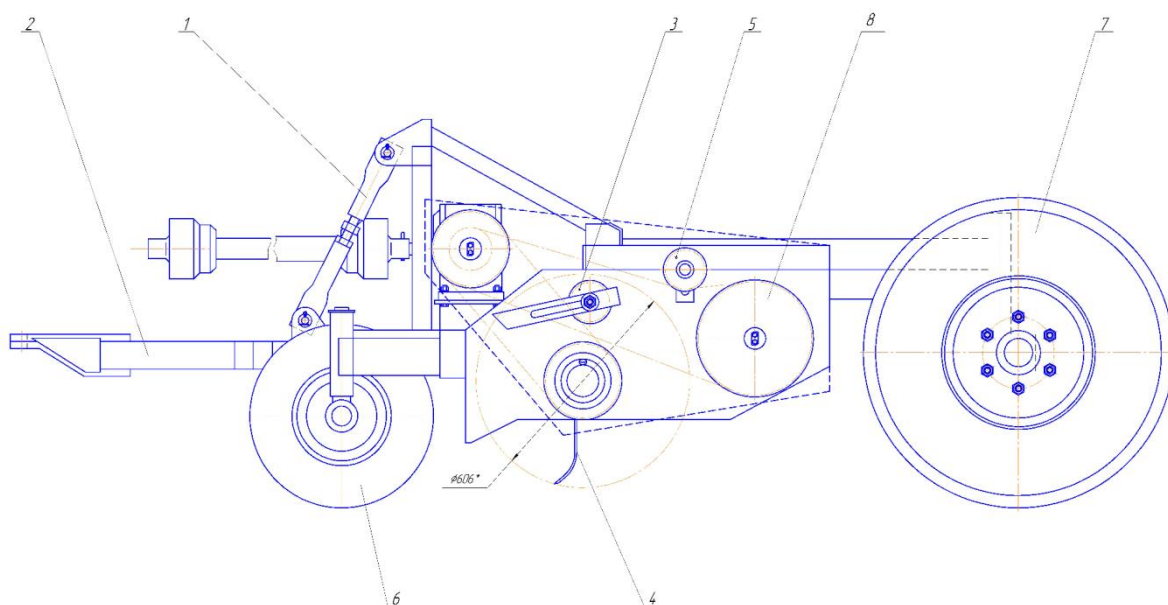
Гичкозбиральна машина МГ-6: 1 – регулювальний гвинт, 2 – сниця, 3, 5 – зірочка натяжна, 4 – барабан (ротор), 6 - опорне колесо, 7 – заднє колесо, 8 – шнек.
